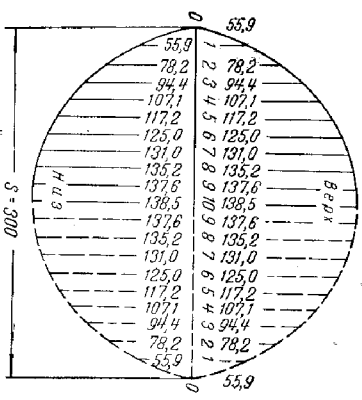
Развертка отверстия в створе сварного трюиника.
